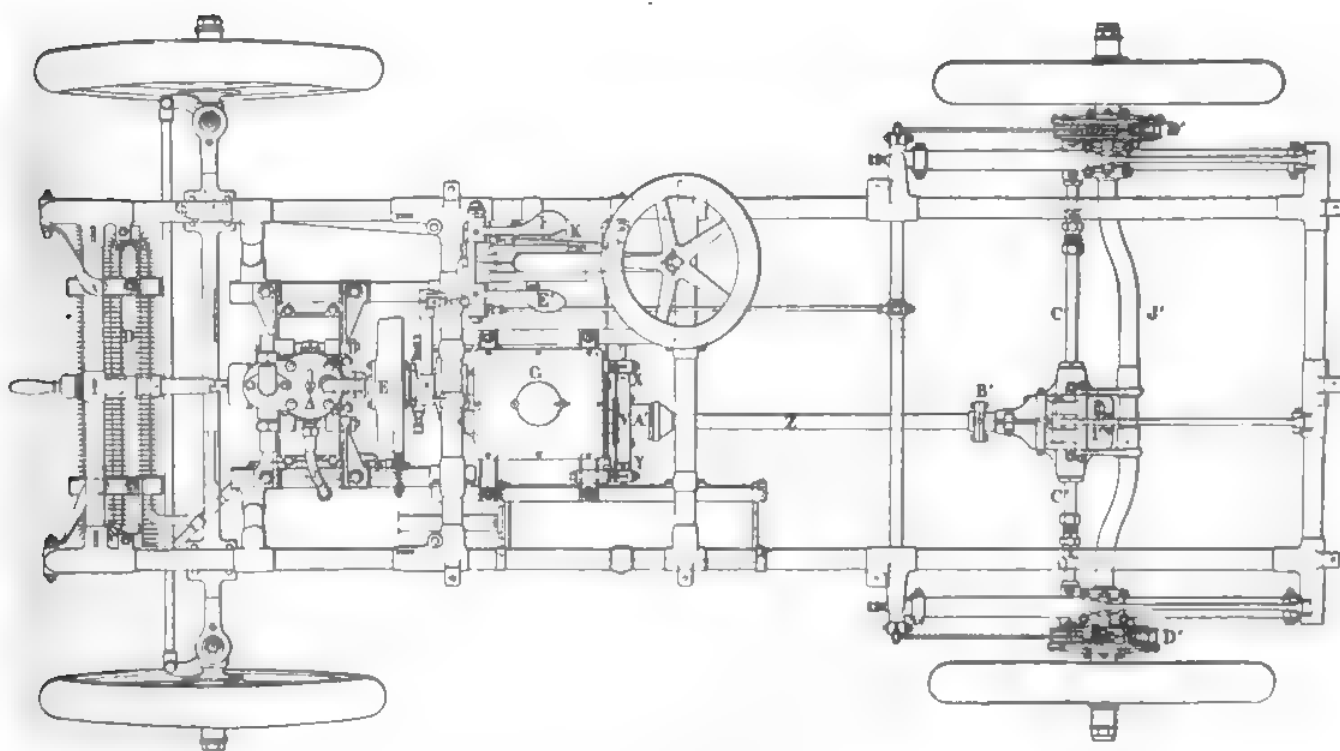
Grundriss des Hurtu-Wagens.
